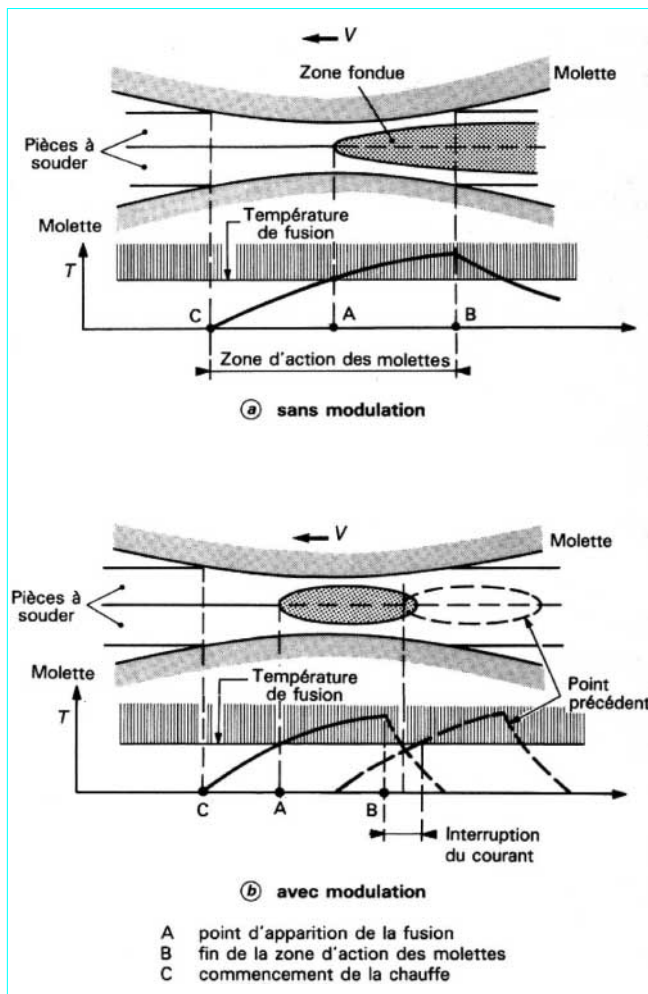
Soudage à la molette : formation de la soudure
